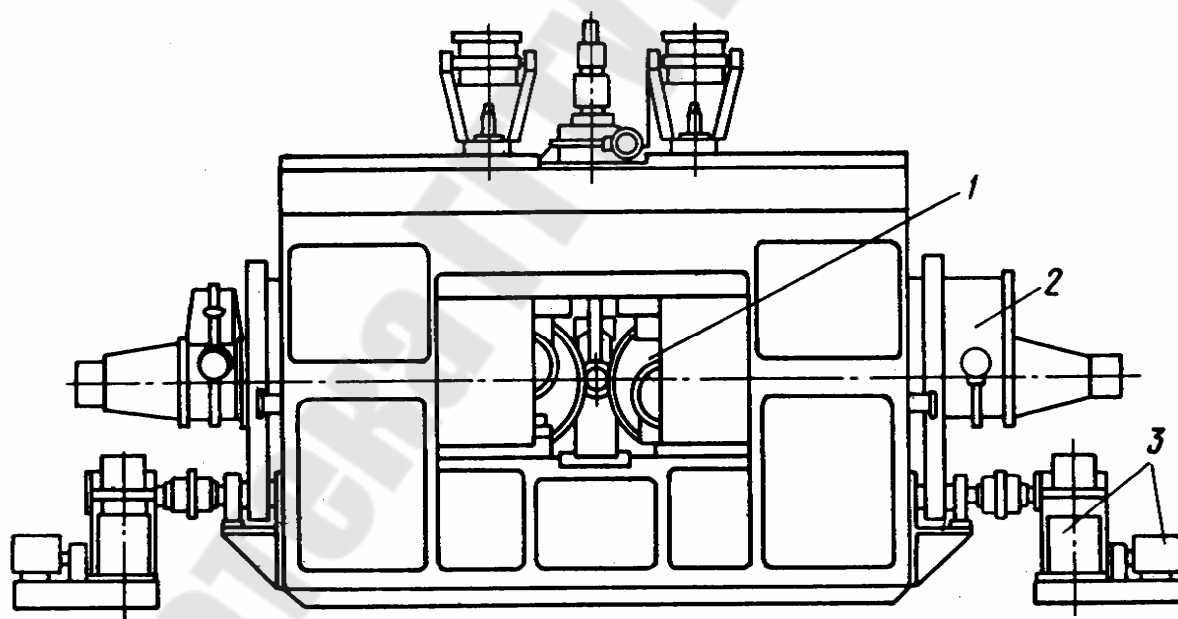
Рабочая клетка прошивного стана с бочковидными валками:
